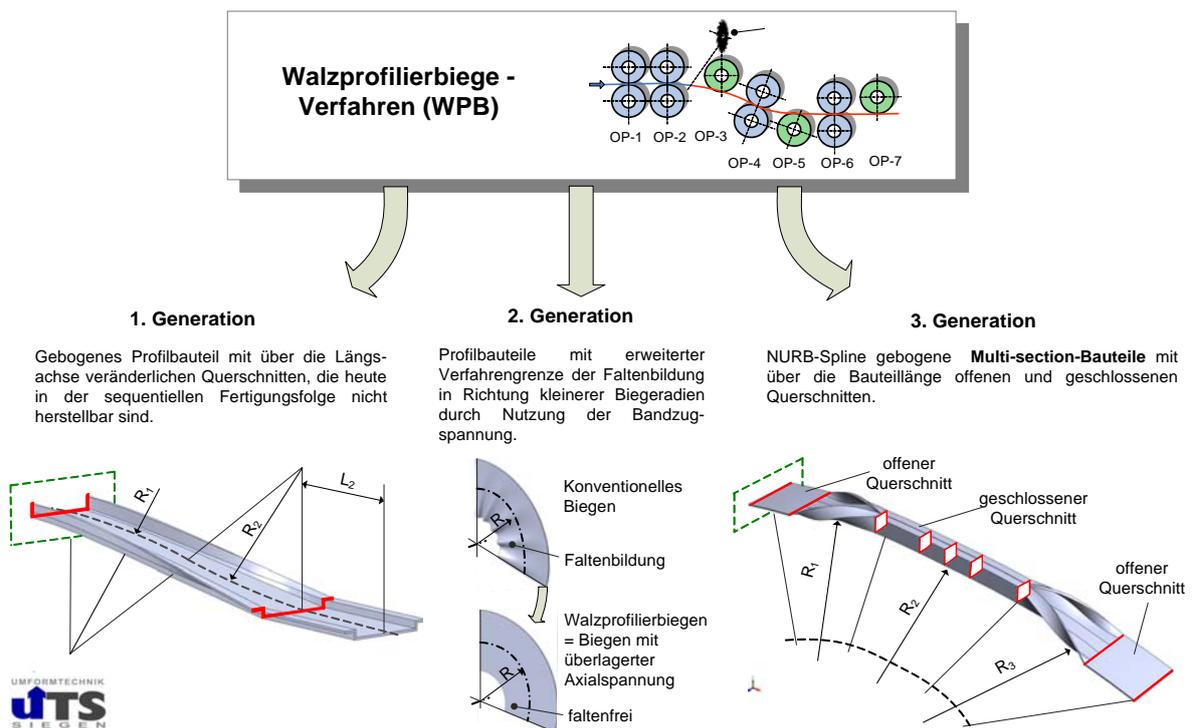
Darstellung zukünftiger im Walzprofilierbiegeverfahren (WPB) hergestellten Profilbauteile
